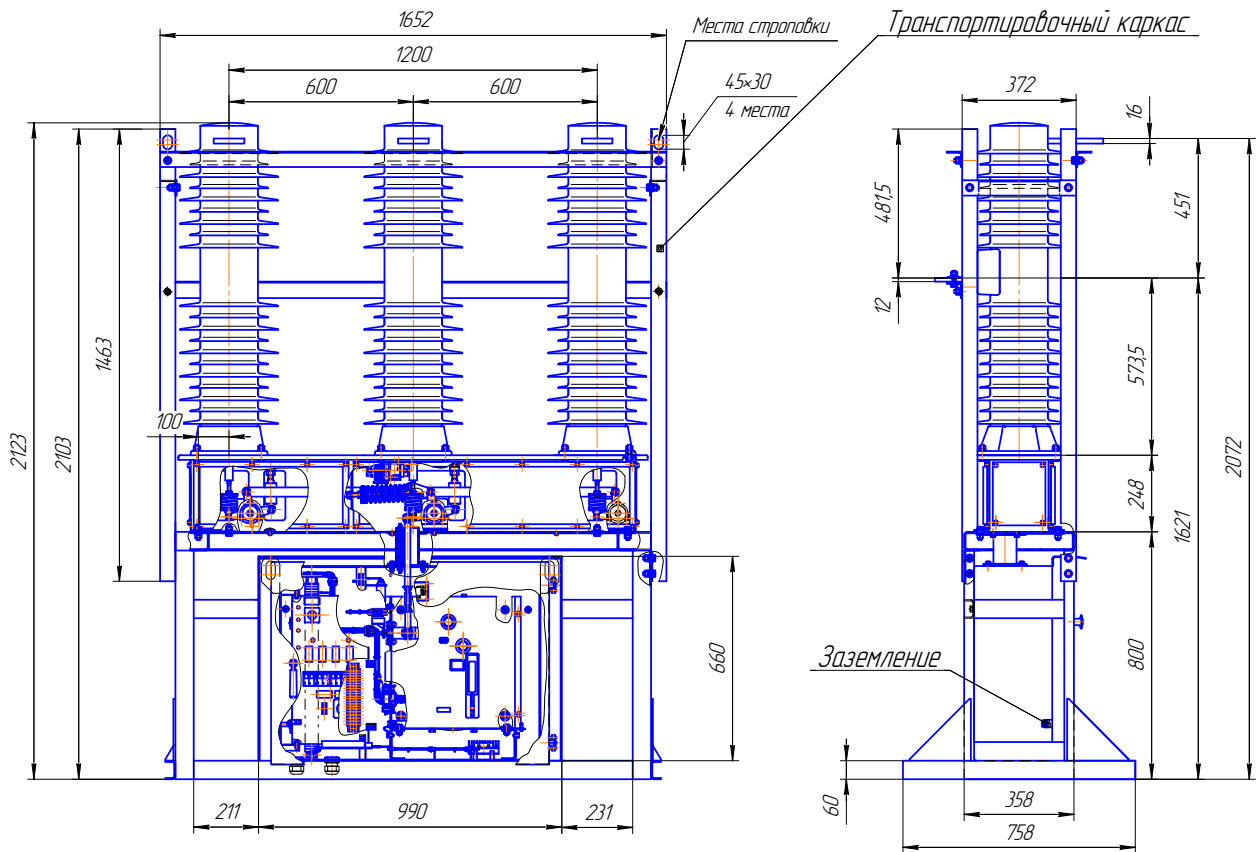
Габаритные, присоединительные и установочные размеры выключателя типа ВВН-СЭЩ-П-35
